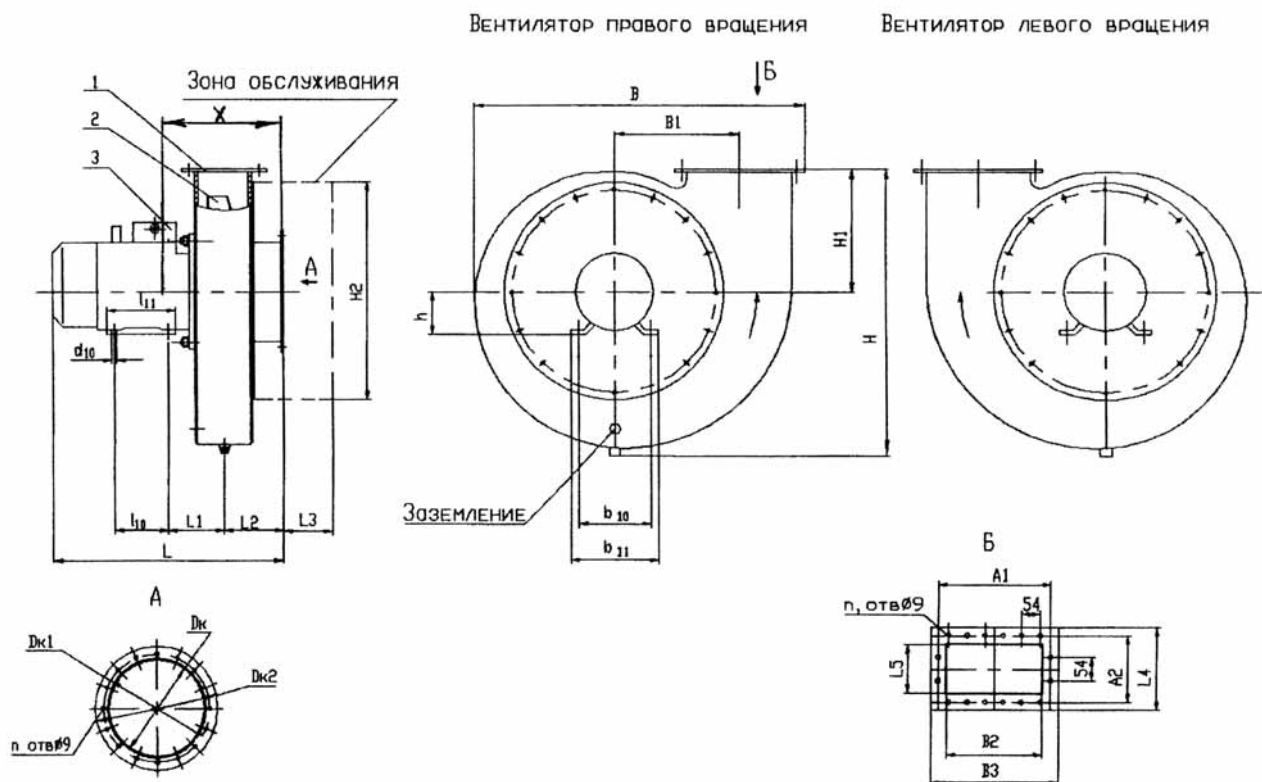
1 – корпус; 2 – колесо рабочее; 3 – двигатель
